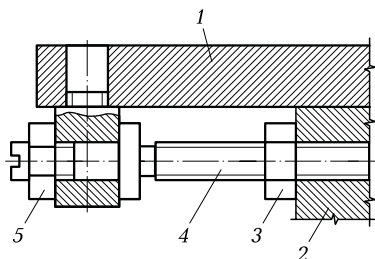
Регулирование зазора между направляющими стола и направляющими каретки консольно-фрезерного станка:
